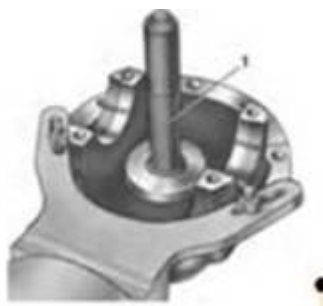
Установка с помощью оправки наружного кольца заднего подшипника ведущей шестерни: 1 — оправка А.70171.
